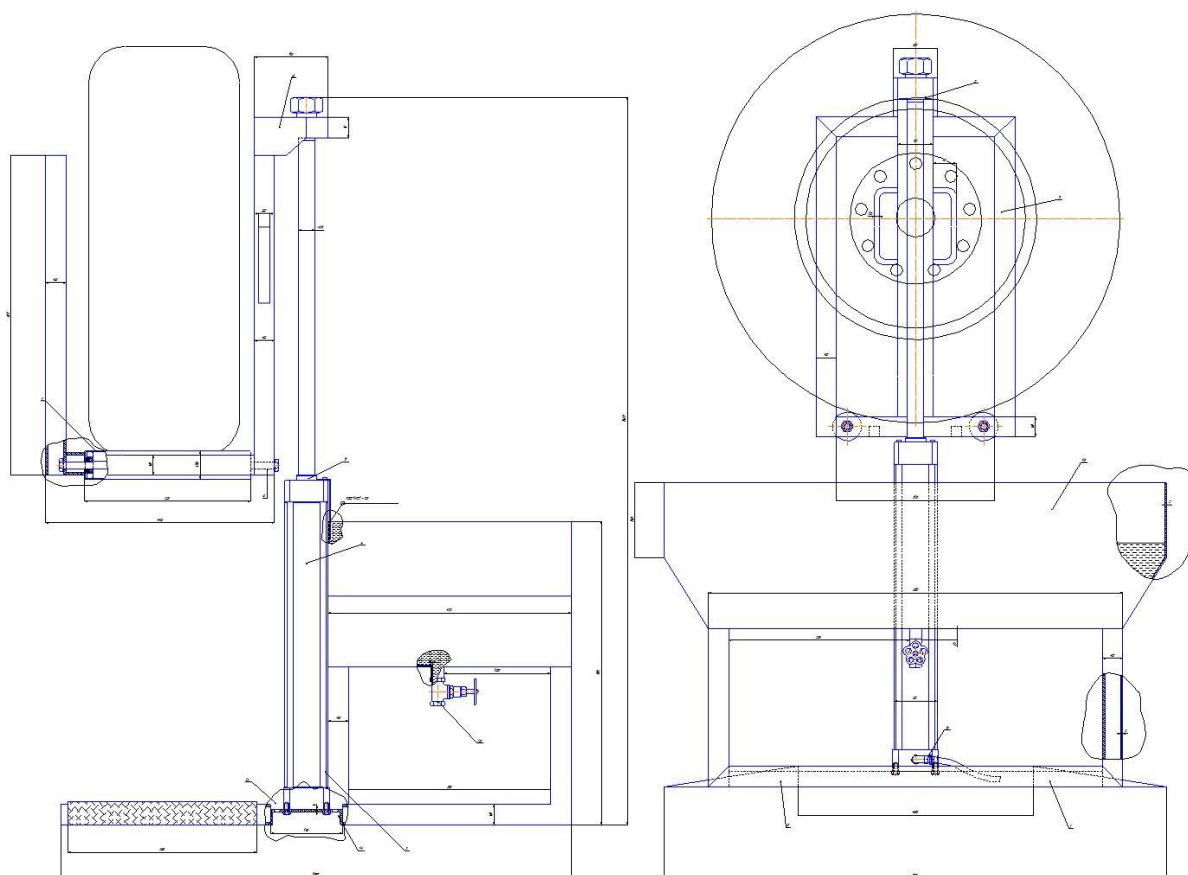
Установка для проверки герметичности колес и камер
